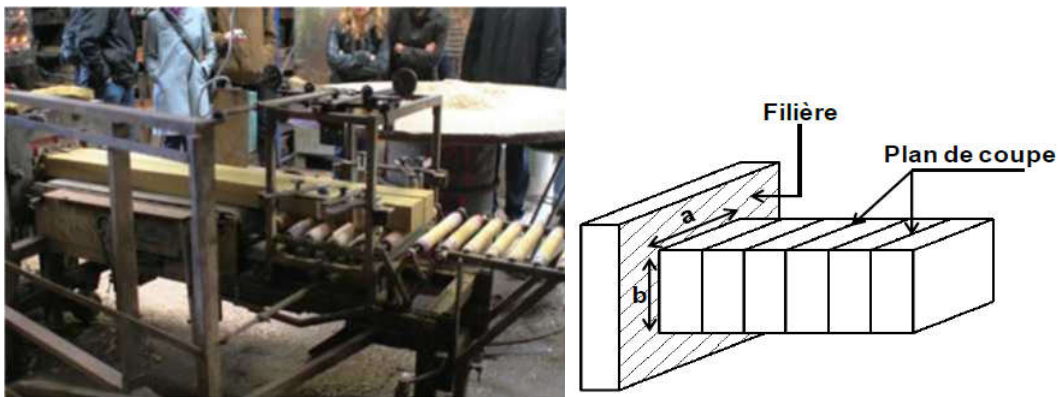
Façonnage de la brique, sens d'extrusion et plan de coupe
